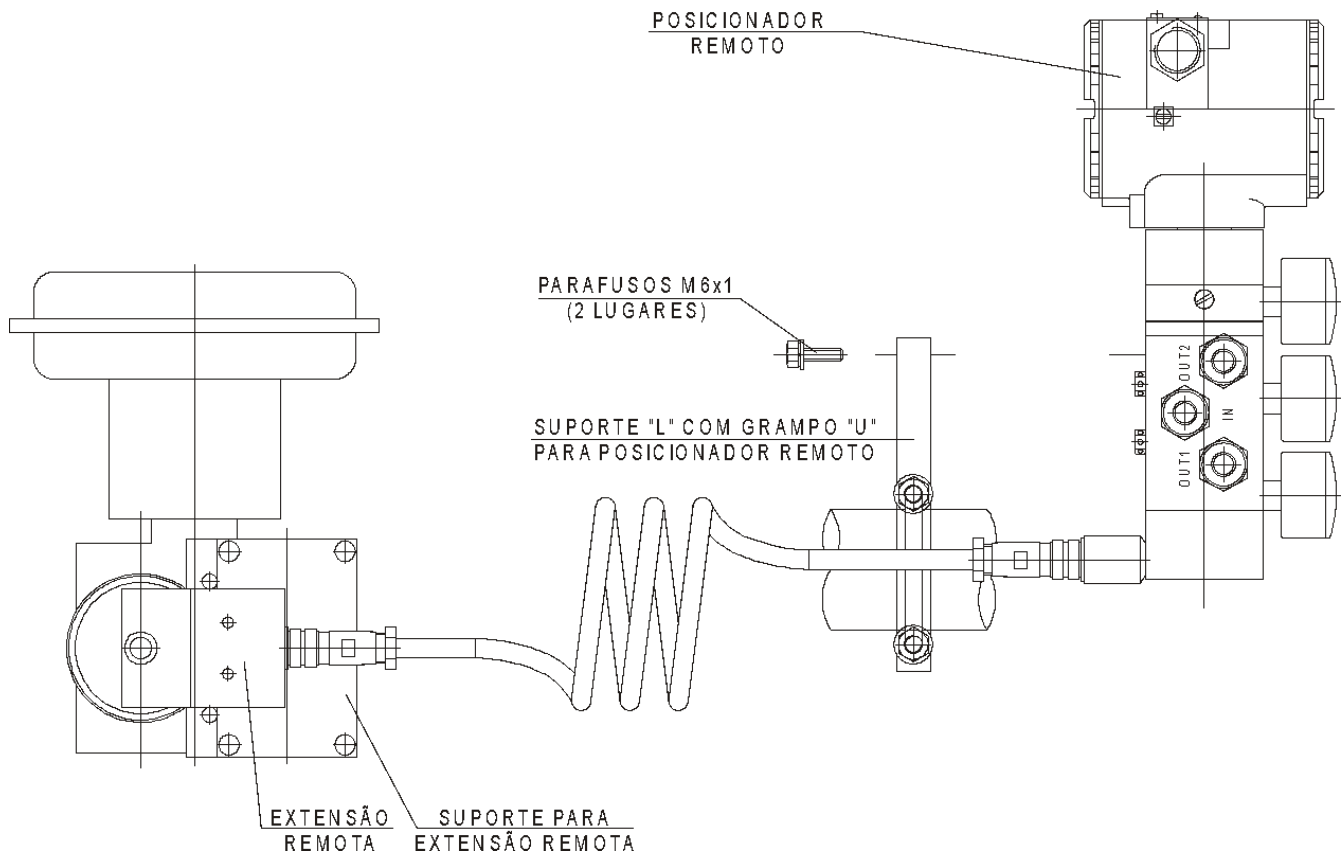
Posicionador em Atuador Rotativo com Sensor de Posição Remoto
